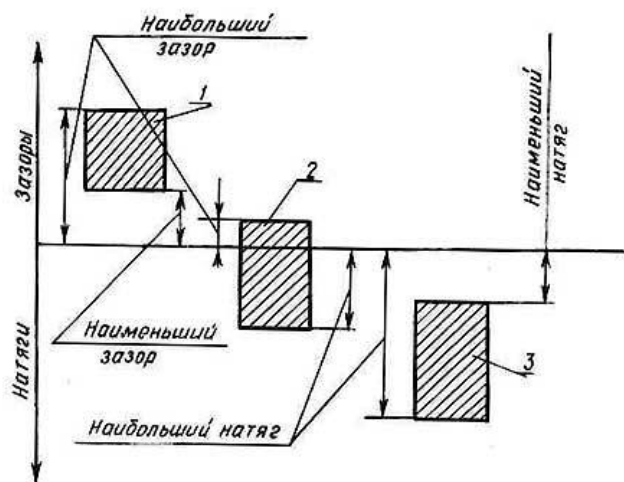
Схема полей допусков для посадок с зазором, натягом
